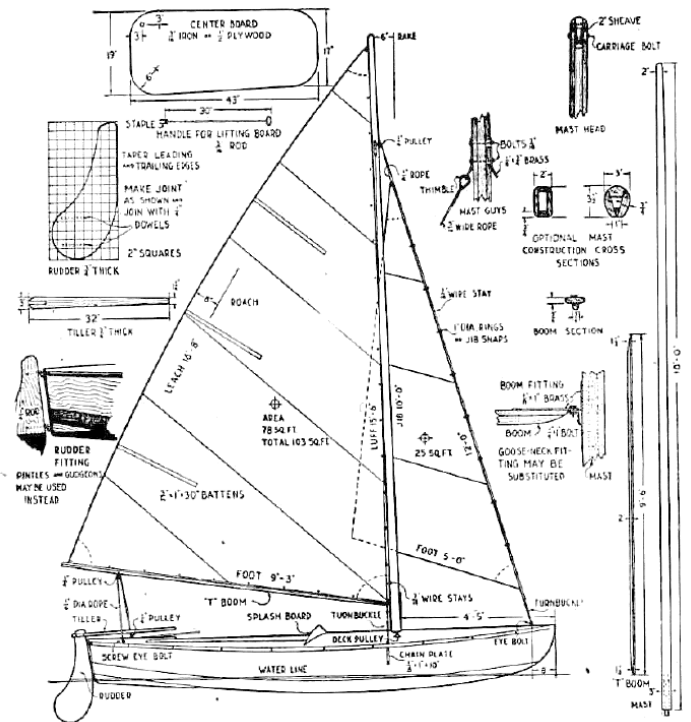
124 Planos Dart Fast (Fuente: Svensons.com)
